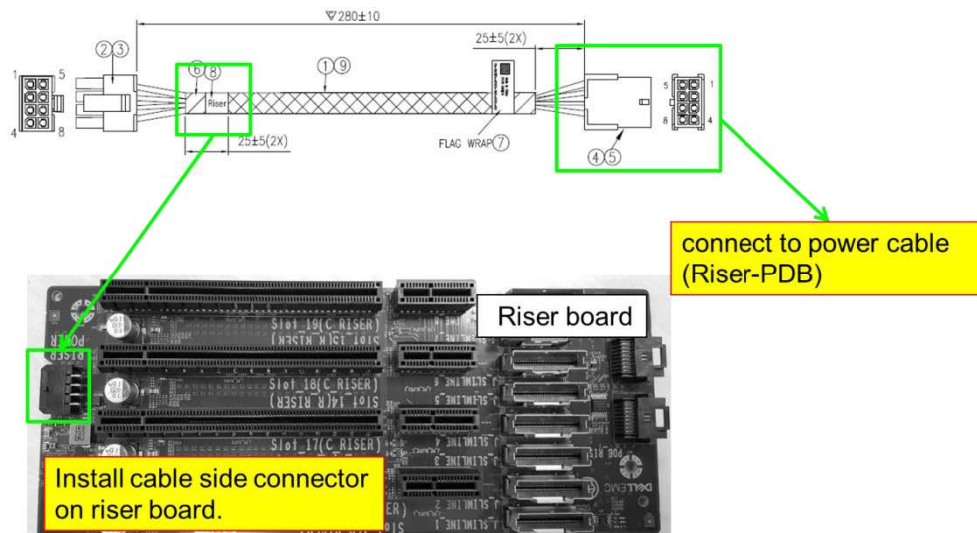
Assemblage du câble d'alimentation 1 vers carte de montage 1
